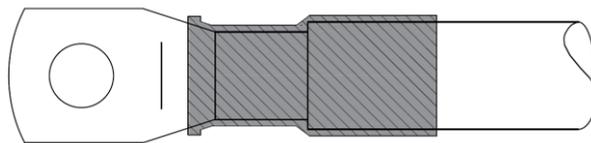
Пример применения термоизоляционной трубки для изоляции соединения кабельного наконечника и силового кабеля
